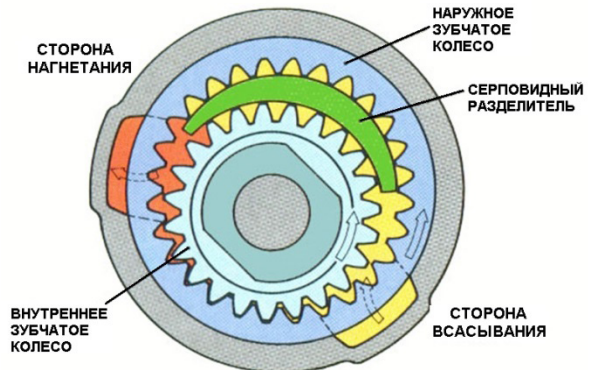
Шестеренчатый насос с внутренним зубчатым зацеплением и серповидным разделителем; источник: *Kraftfahrzeugtechnik TAK
